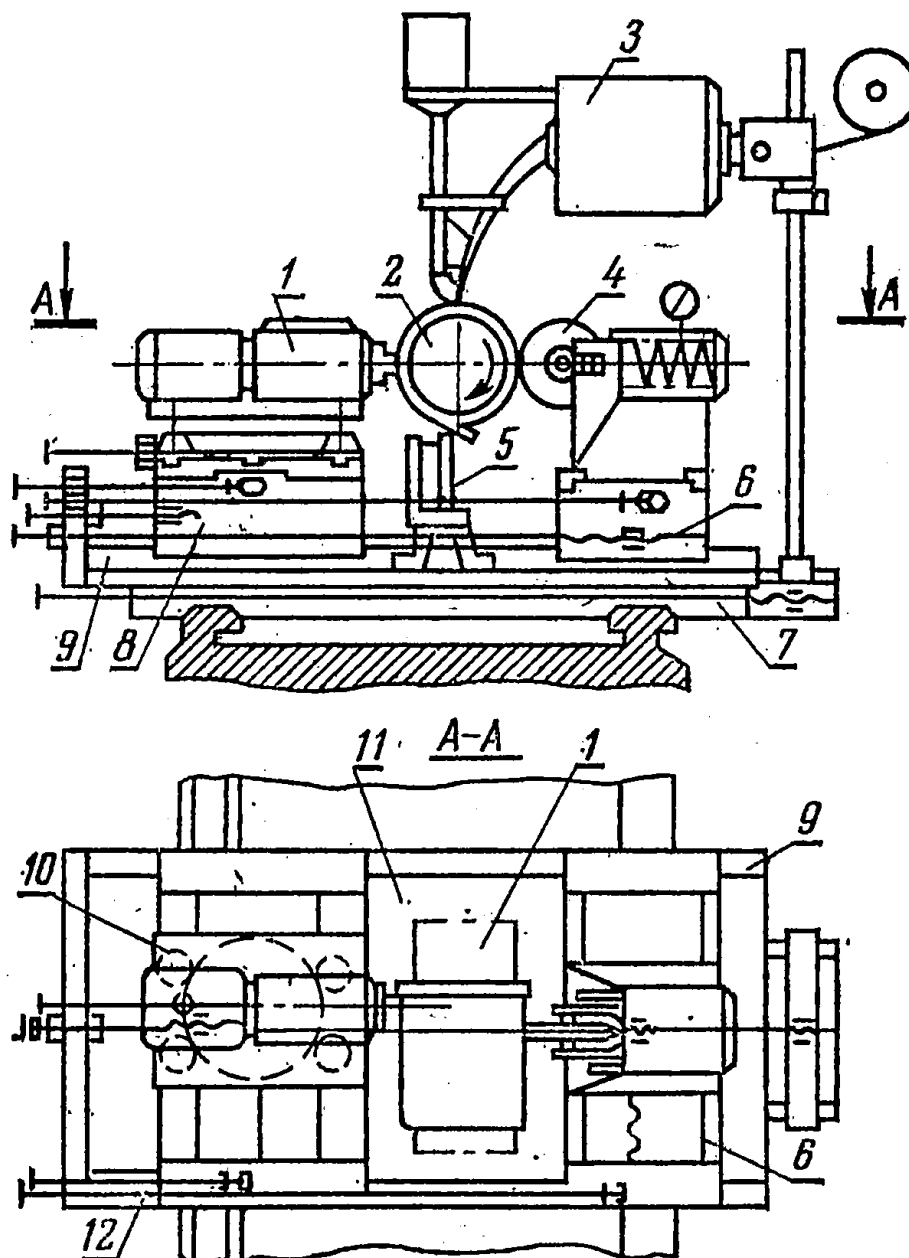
Схема установки для наплавки цилиндрических деталей под флюсом с одновременным фрезерованием и накаткой роликом:
